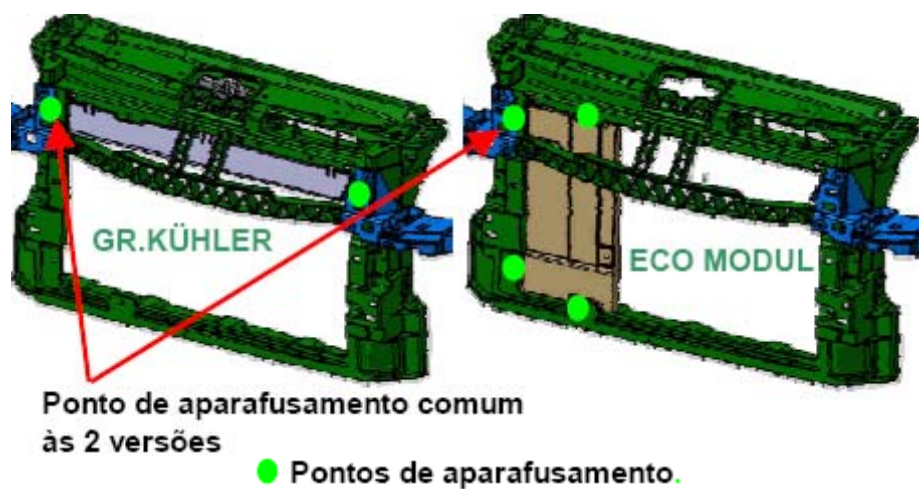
À esquerda a versão GR. KÜHLER com o ADAPTER GROSSE KUEHLER, à direita a versão ECO MODUL com o ADAPTER ECO MODUL
